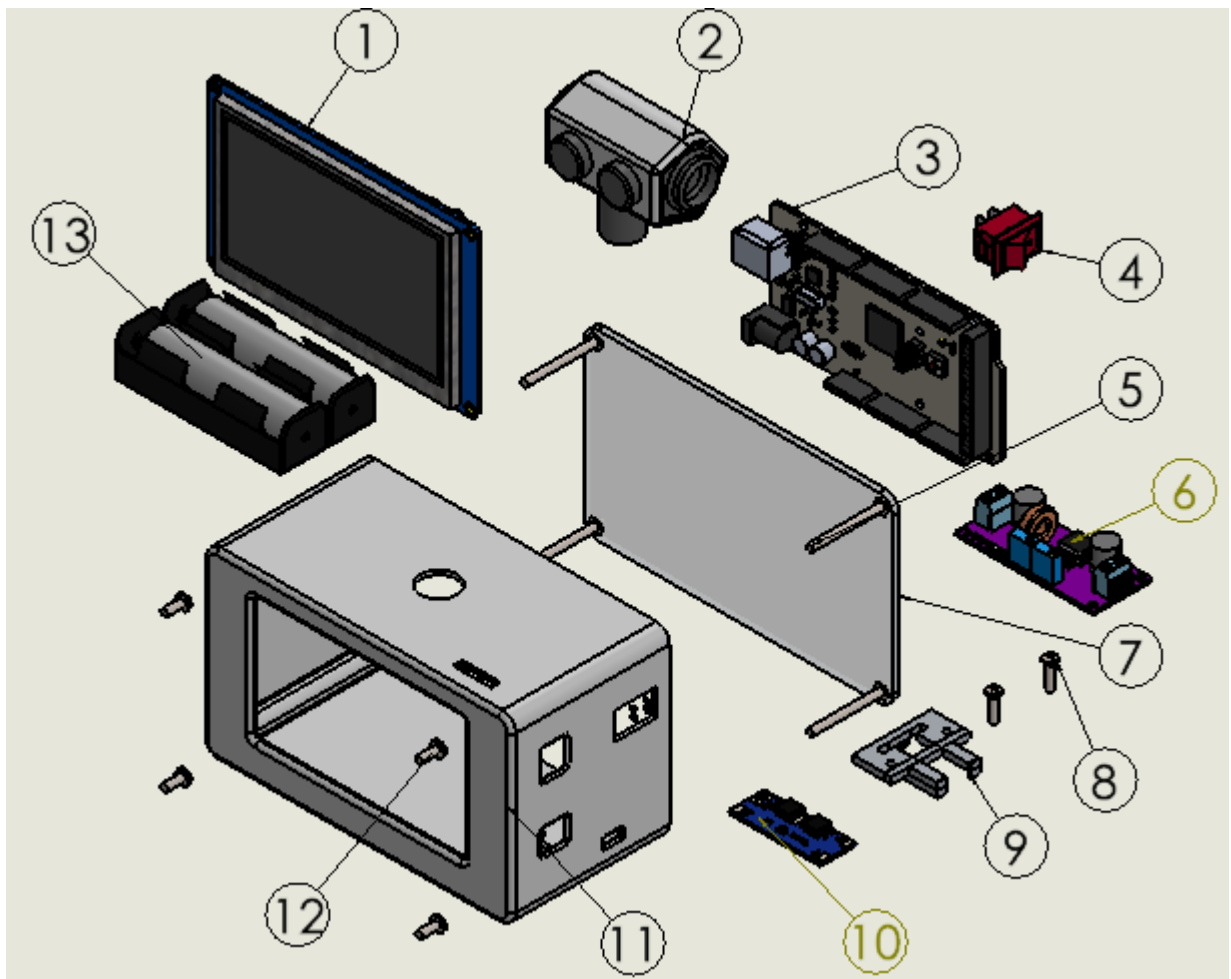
Vista isométrica explosionada de la solución propuesta
